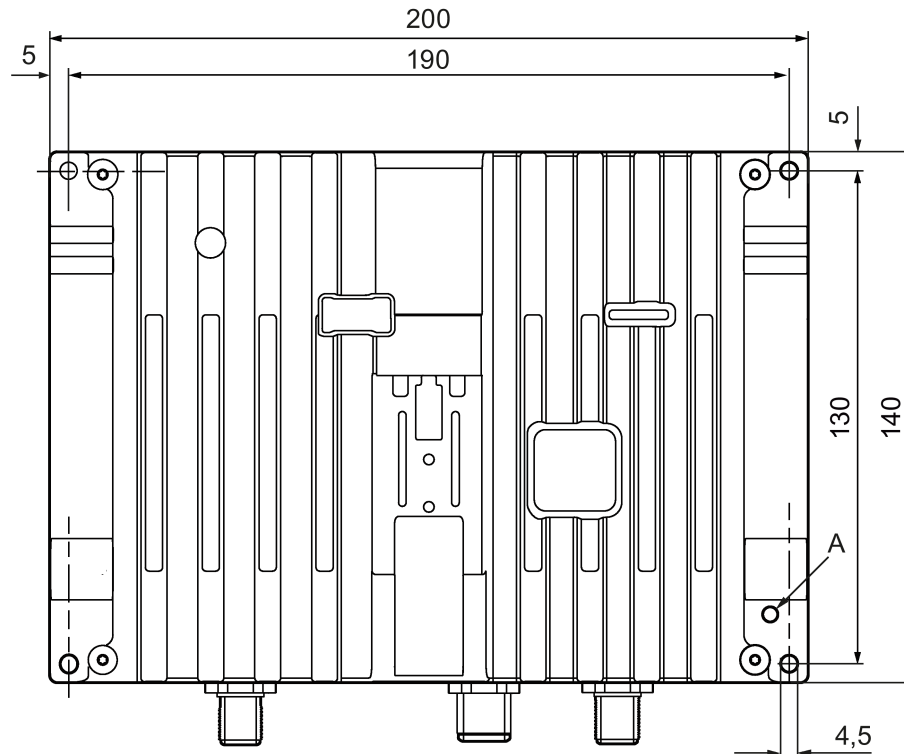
Matriz de perfuração do RF290R (dimensões em mm)
